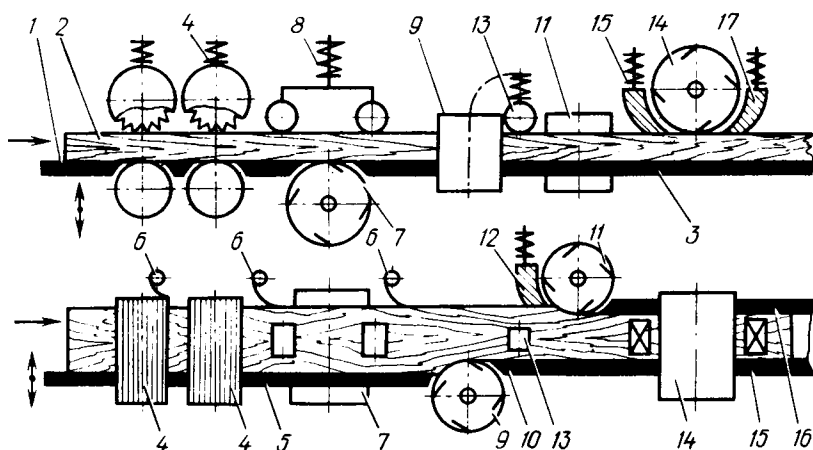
Схема четырехстороннего продольно-фрезерного станка:
